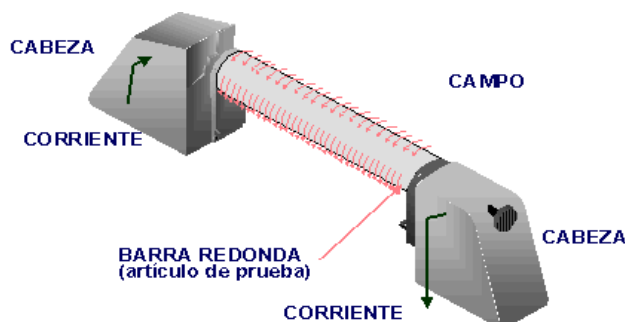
Empleo de la técnica de cabezales para piezas cilíndricas.
